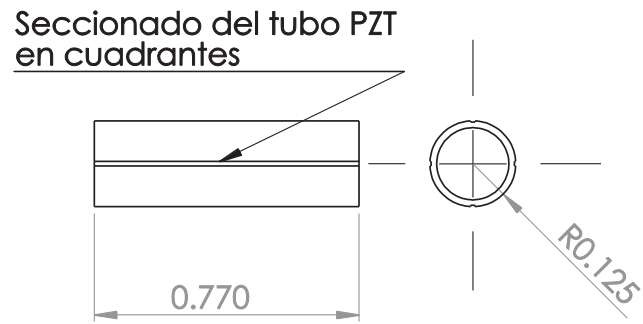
Dimensiones del piezoeléctrico seccionado en cuadrantes.
